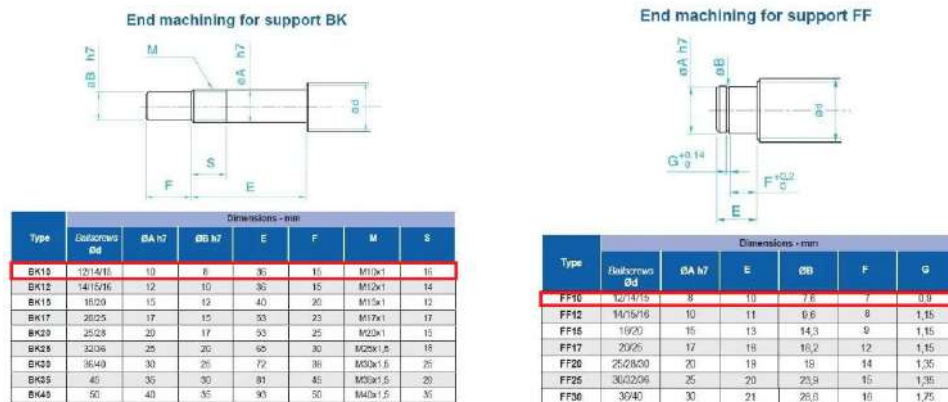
Diseño de extremos del tornillo para el montaje.
